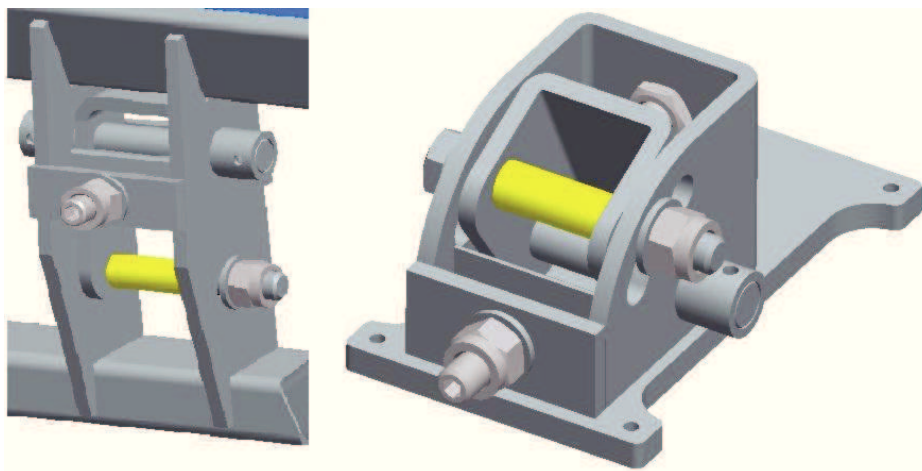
Obdélníkový profil pro zadní část motoru č. 2
